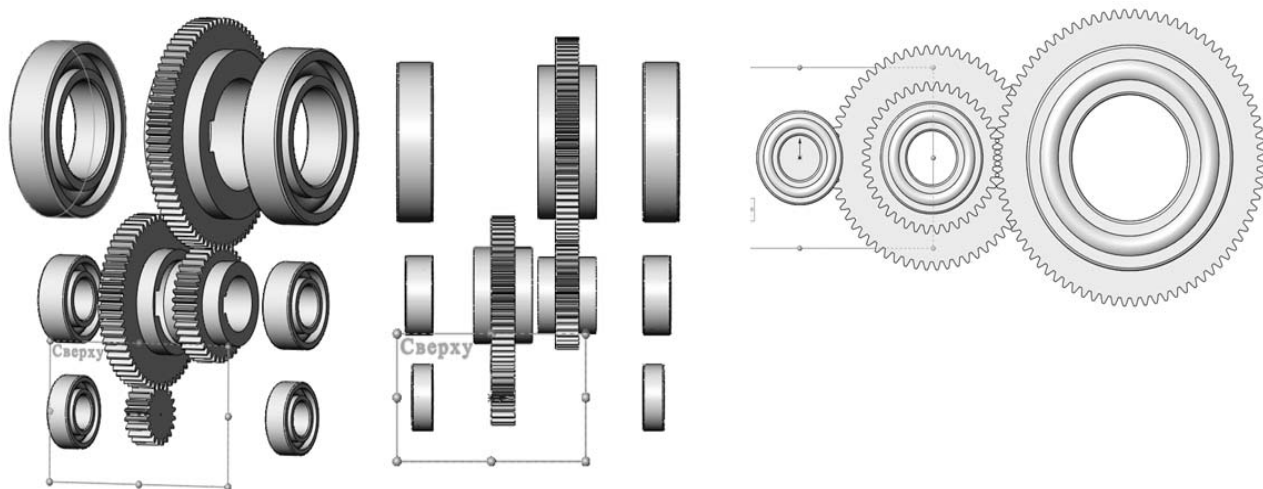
3D-модель сборки редуктора с подшипниками качения
